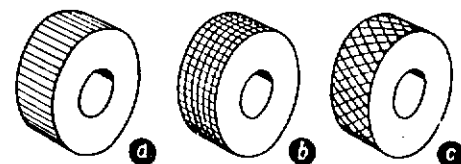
,1. Piezas moleteadas: a) Moletado paralelo; b) moletado en cruz; c) moletado en X.
